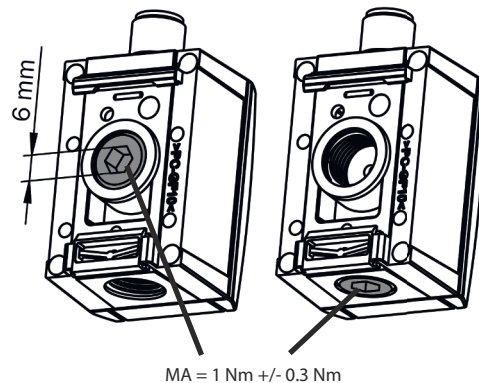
Druckanschluss G 1/4-Innengewinde
